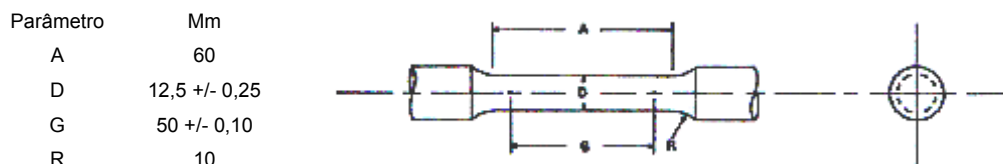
Corpo de prova de tração com dimensões padrões, usinado conforme norma ASTM designação A370[43].
